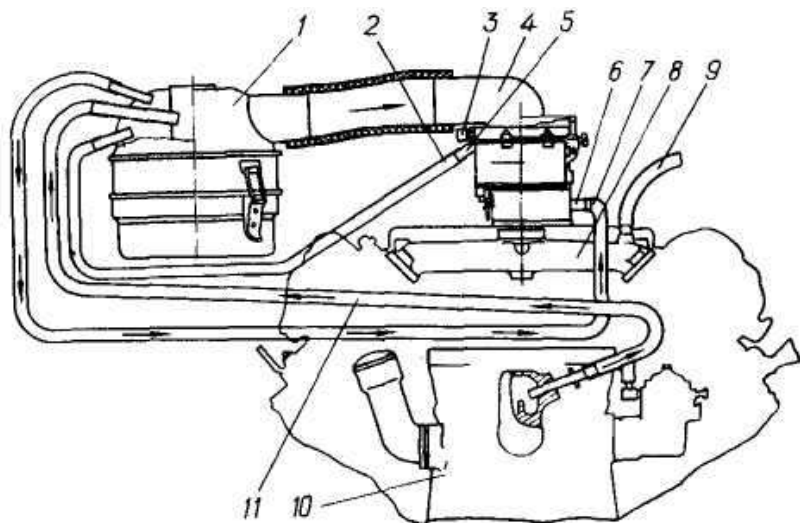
Схема отсоса картерных газов и разбалансировки поплавковой камеры карбюратора:
